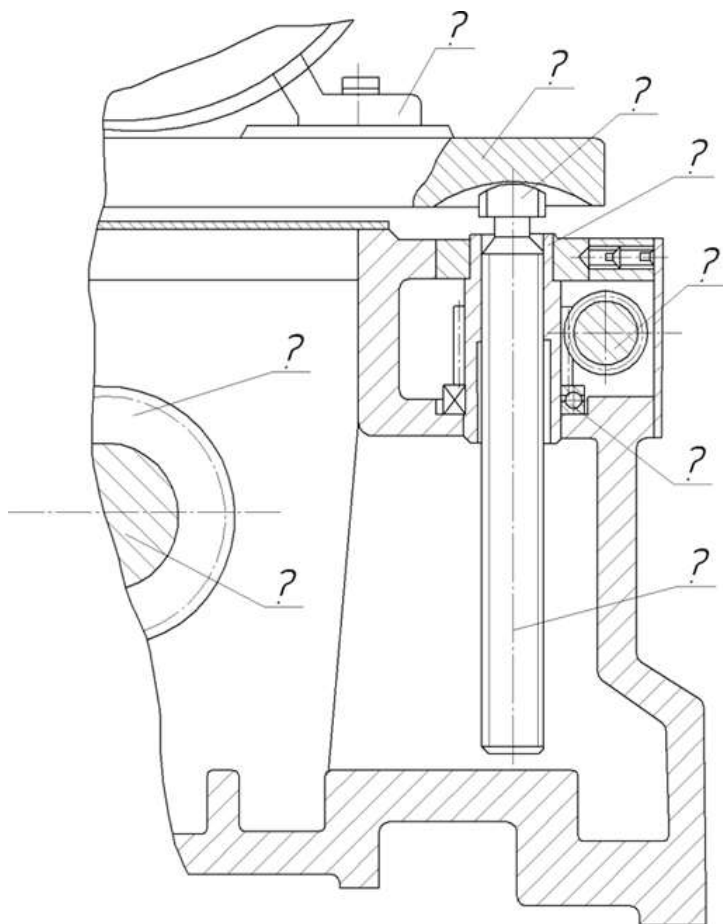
Пристрій для натягання пасової передачі між шківками А та Б
